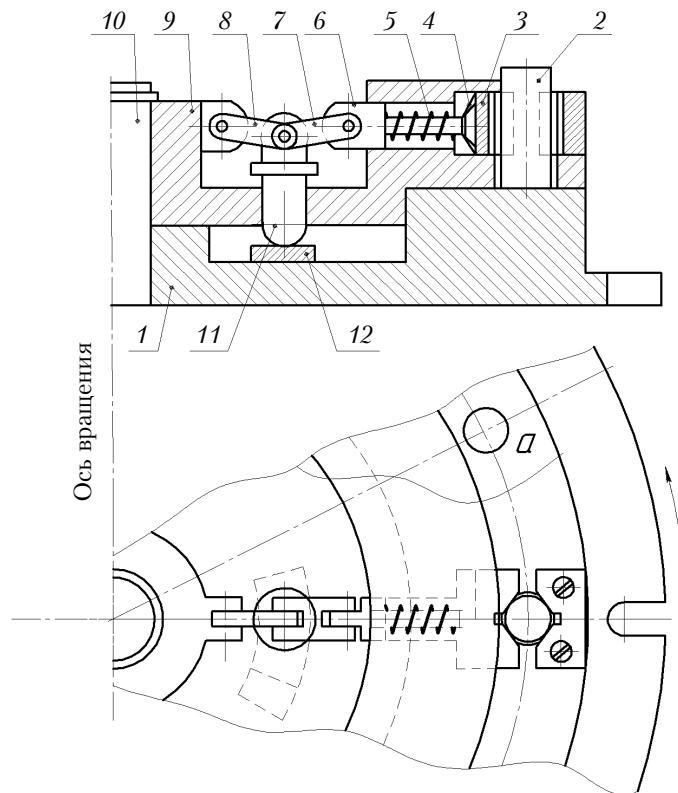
Схема зажима заготовок на столе карусельно-фрезерного станка с приводом от вращения стола
